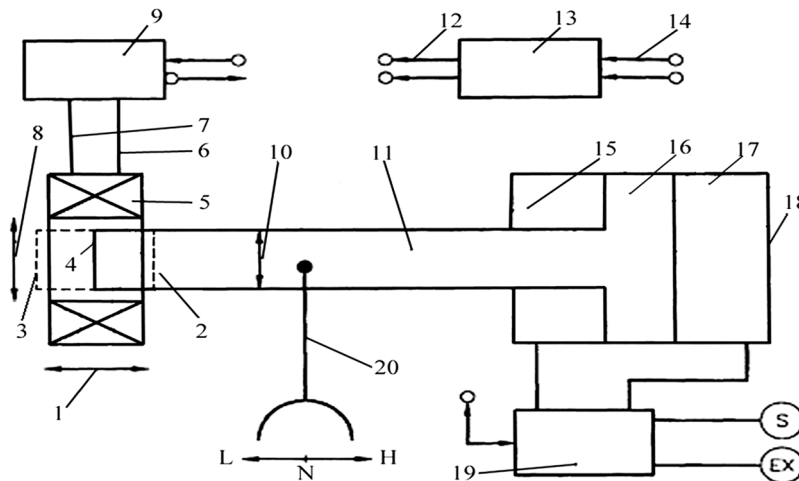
Исполнительный механизм дополнительной коробки передач: 1, 8 — ширина и внутренний диаметр катушки 5; 2, 3, 4 — положения концевой части штока 11 соответственно в позициях Н-Н-Л; 6, 7 — концы обмоток катушки 5; 9 — измерительное устройство с регулятором напряжения; 10 — диаметр штока 11; 12, 14 — соответственно выходные и входные сигналы микропроцессорного блока 13; 15, 17 — рабочие полости гидроцилиндра 18; 16 — поршень; 19 — блок ЭМК; 20 — вилка включения передачи; S, EX — нагнетательная и сливная магистрали
